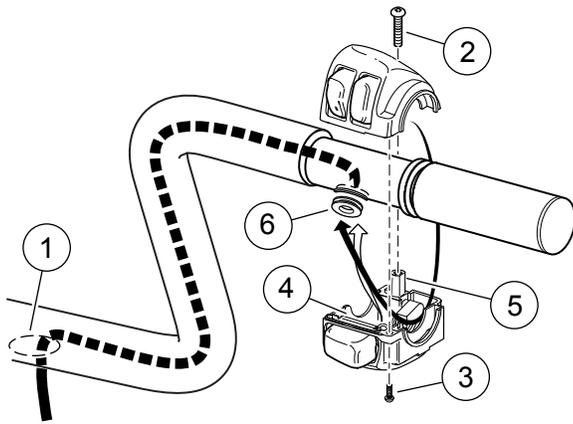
Прокладка проводов указателя поворота и переключателя через корпус переключателя
